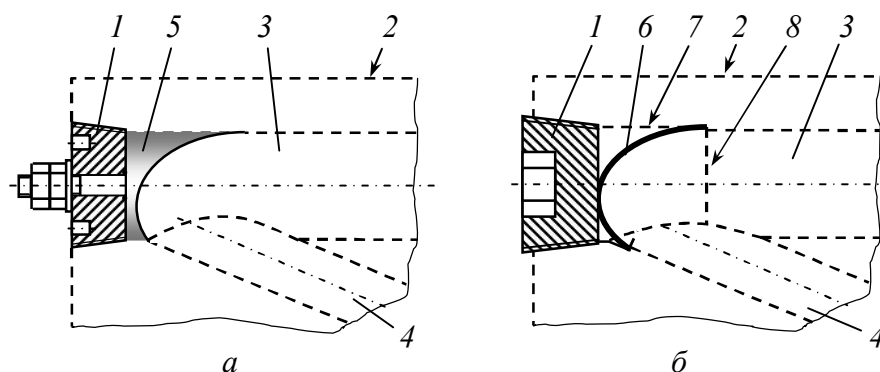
Конструкції обтічників, що знижують гідравлічний опір валків: а – згідно з пат. України № 27697 У [103]; б – згідно з пат. України № 43734 У [104]; 1 – торцева нарізна пробка; 2 – робоча поверхня бочки; 3, 4 – периферійний і похилий канали; 5 – циліндрична насадка; 6 – пружна вставка; 7, 8 – розточення периферійного каналу і її уступ
